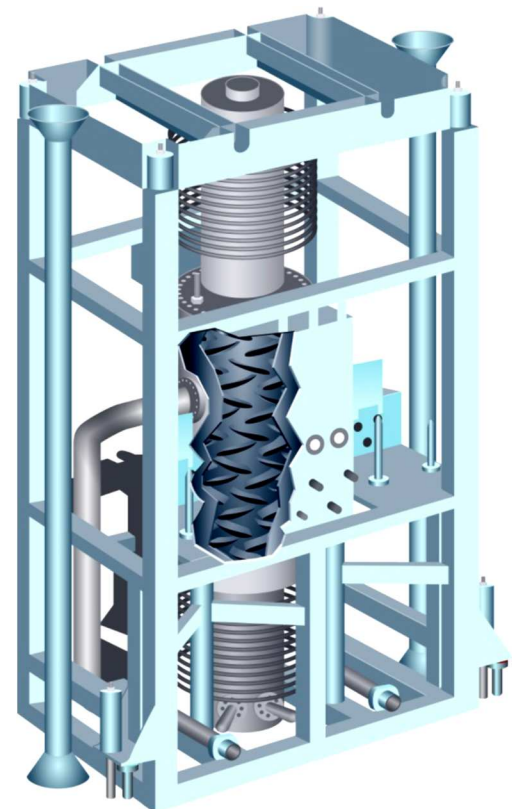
3D-модель компрессора WGC 4000, ф. One Subsea
